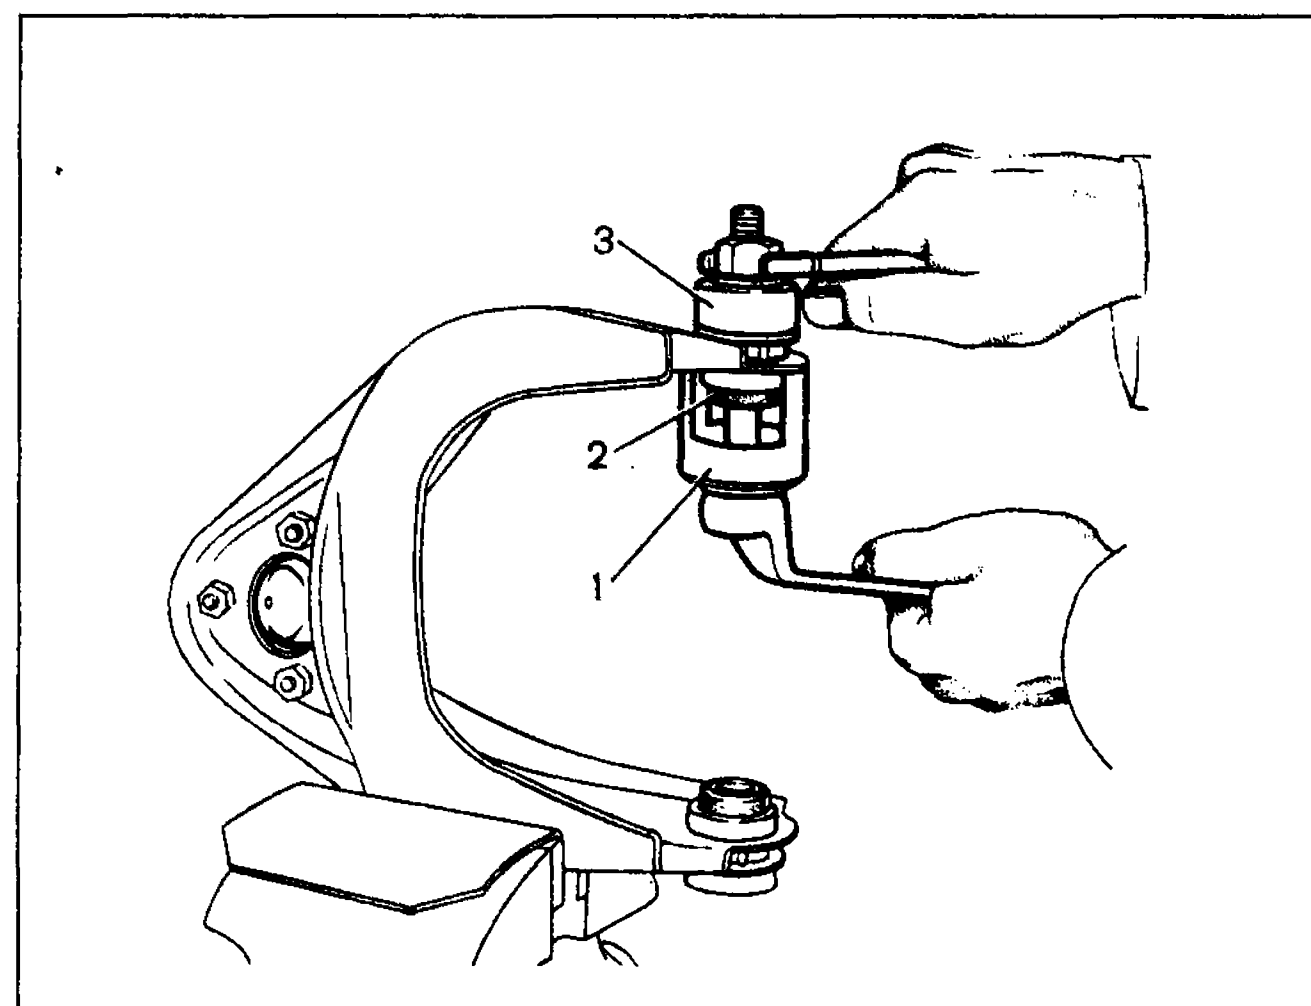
Запрессовка шарниров нижнего рычага:
